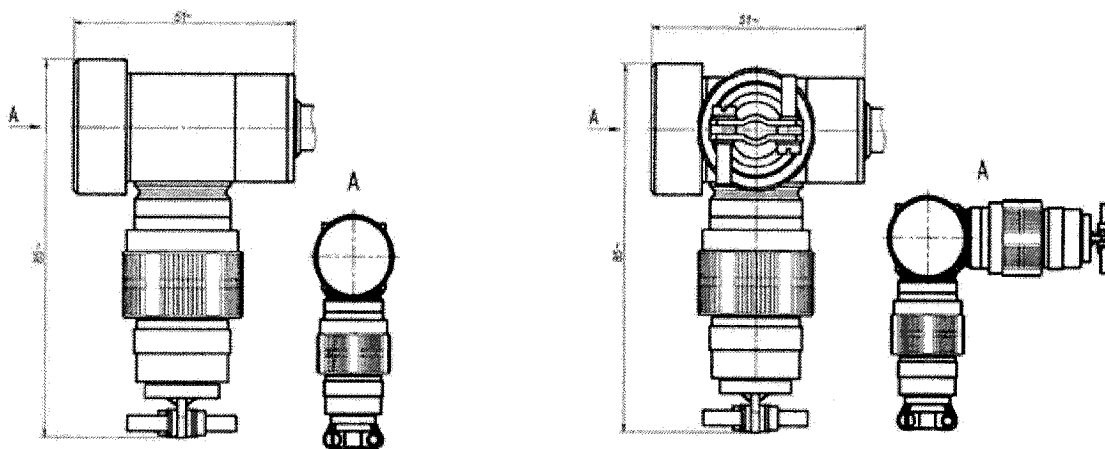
Кресленик зовнішньої частини ТХА-1690, ТХК-1690 з головкою типу БАУИ.4087234.023 СБ
